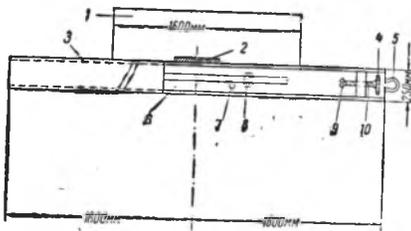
Станок с подвижной кареткой с зажимами (вид сверху без ограждения пр. ножа): 1 — стол; 2 — диск пилы; 3 — полозки для каретки; 4 — маховичок; 5 — ручка каретки; 6 — подвижная каретка с зажимами; 7 — рукоятка крепления; 8 — зубчатая гребенка; 9 — зубчатый зажим; 10 — трехзаходный винт.
